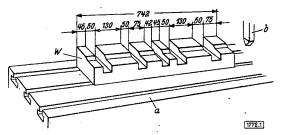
Hobelmaschinentisch mit Versuchs-Werkstück a Maschinentisch, b Hobelstahl, W Werkstück
